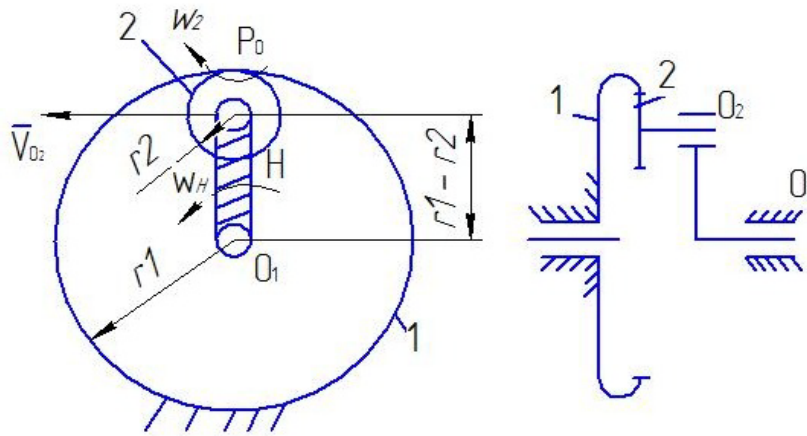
Трёхзвенный зубчатый механизм:
